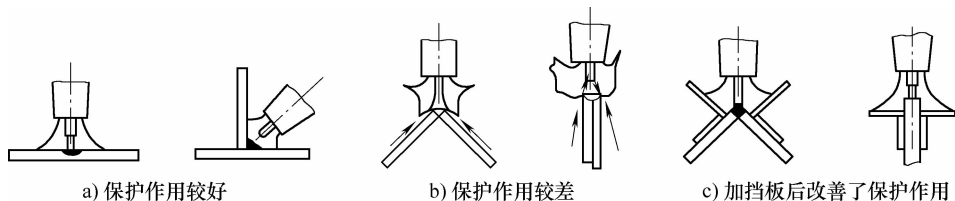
焊接接头形式对气体保护效果的影响
